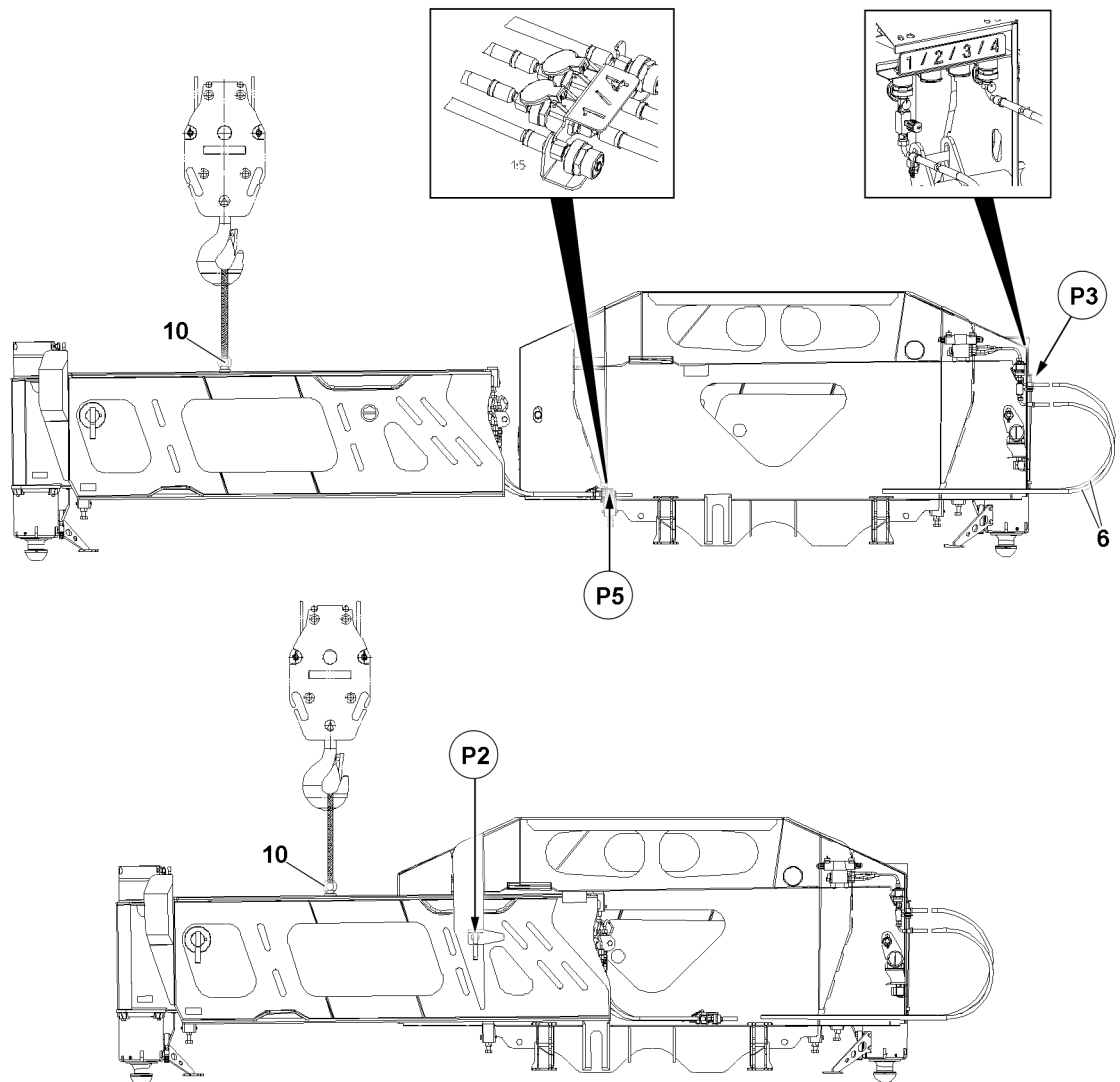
Erguer a viga móvel para a caixa da viga móvel
